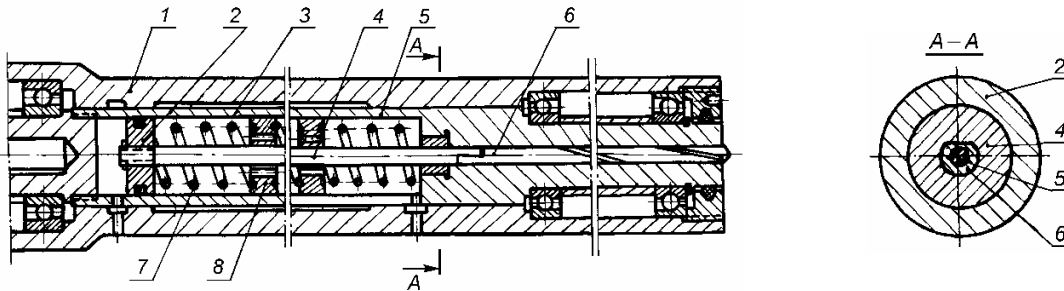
Механізм привода верстатів для глибокого свердління з проміжними опорами
